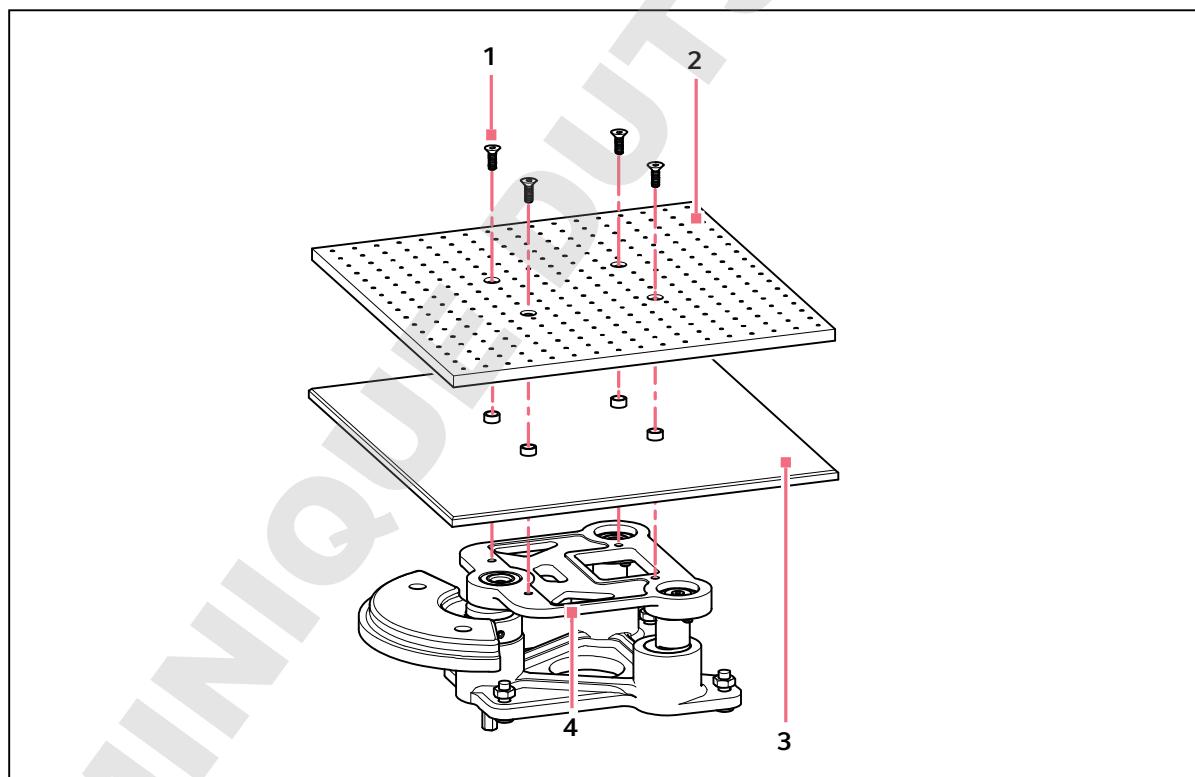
Installer la plateforme et la protection anti-déversement
